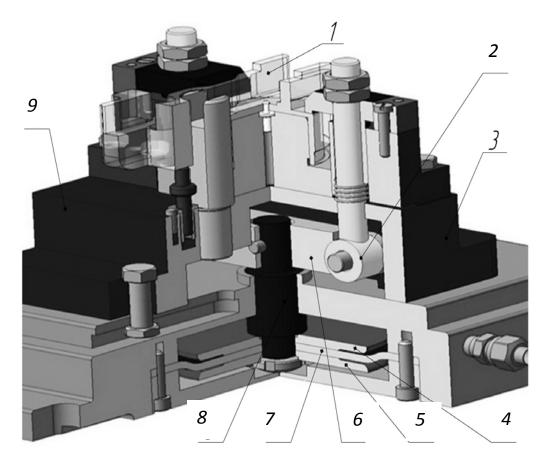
3D-модель станочного приспособления для обработки детали «Корпус» с четвертным вырезом: 1 — заготовка; 9, 3 — прихваты; 2 — скалка; 6 — коромысло; 8 — шток; 4, 5 — диски; 7 — мембрана
